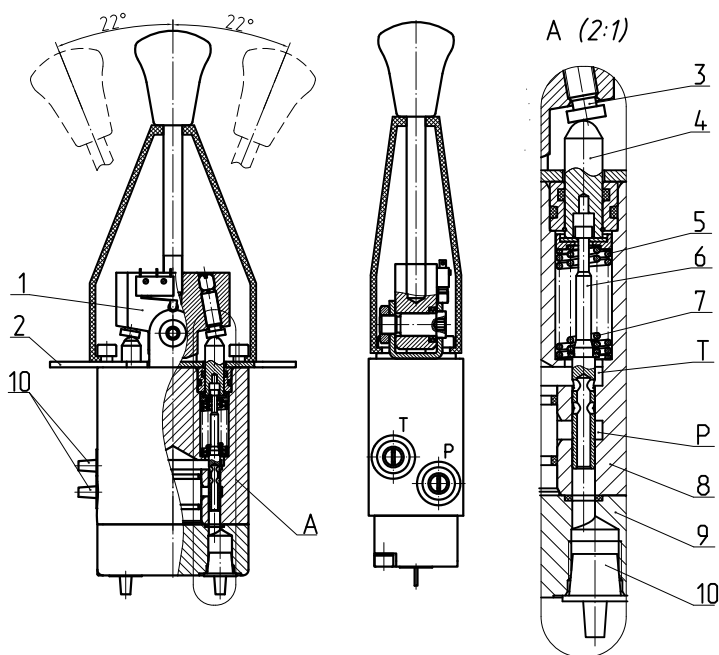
Устройство блока управления где: 1–рычаг; 2–опора; 3–упор; 4–толкатель; 5–пружина возвратная; 6–золотник; 7–пружина регулировочная; 8–корпус; 9–плита; 10–заглушка.
